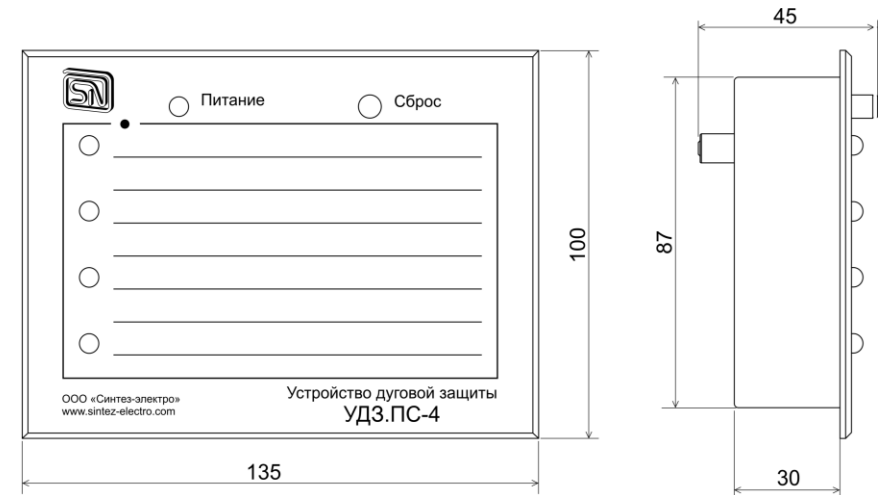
Габаритные размеры УДЗ.ПС-4.УЗ.
